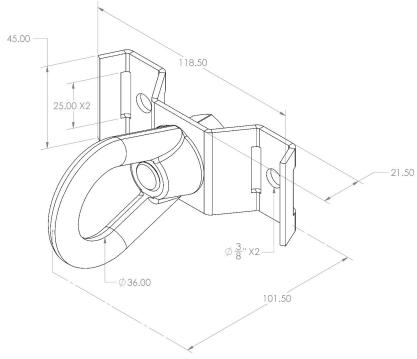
Dimensiones generales del herraje HSP-100-1-3/4.
